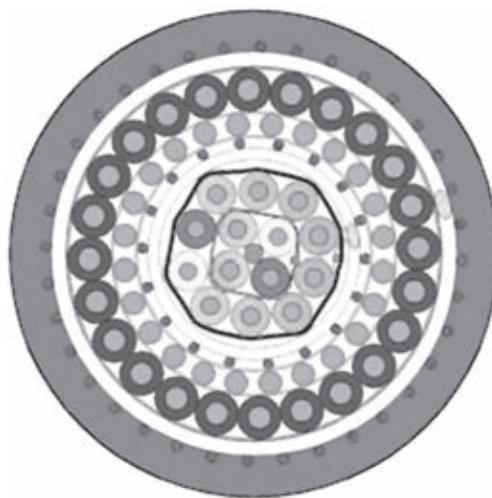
Сечение кабеля для подводной автоматизированной сварки
